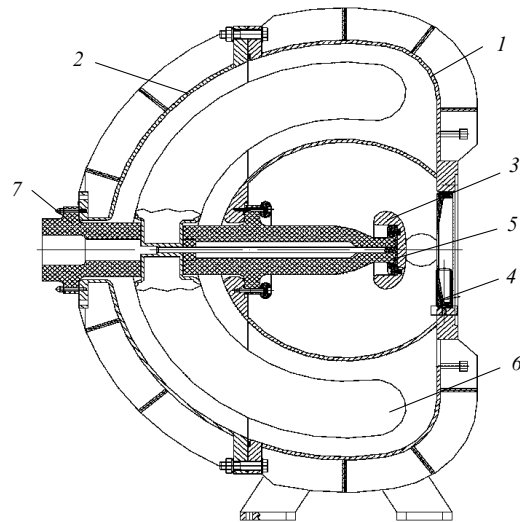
Конструкция разрядной камеры: 1 – внешний корпус; 2 – внутренний корпус; 3 – профилированный электрод (катод); 4 – сеточный электрод; 5 – проходной изолятор; 6 – высоковольтная обкладка водяного конденсатора; 7 – высоковольтный ввод.
